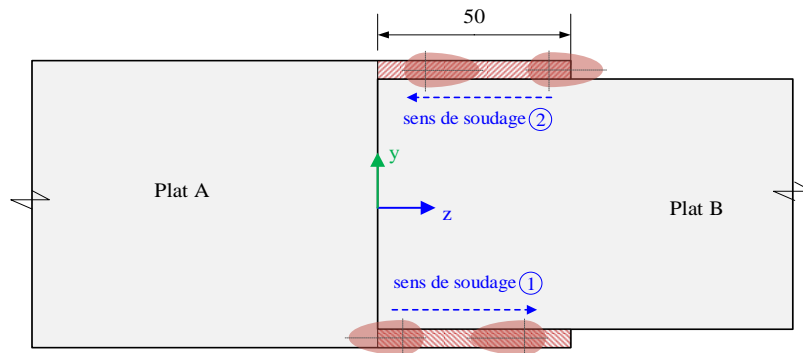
Maillage de l'assemblage par soudure d'angle
